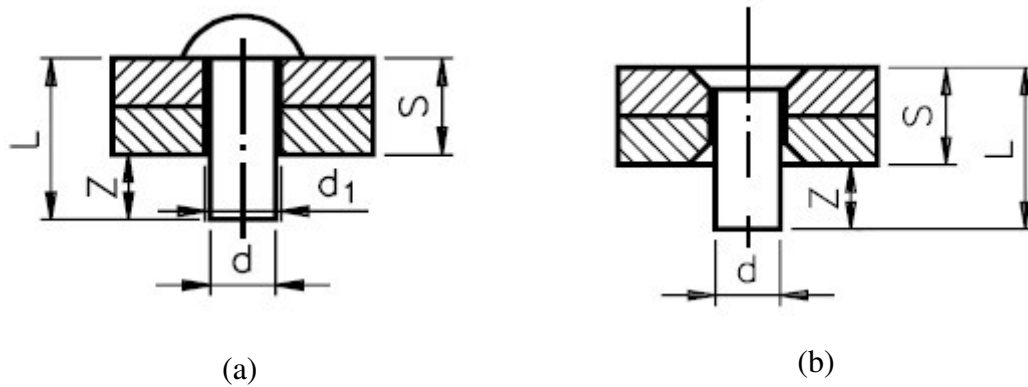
Tipos de rebite: (a) de cabeça redonda; (b) de cabeça escareada.
